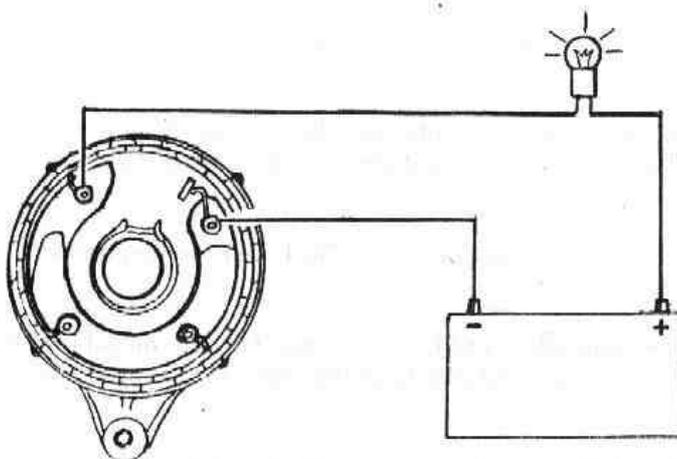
Comprobación del conjunto montado placa rectificadora y arrollamiento (estator)
